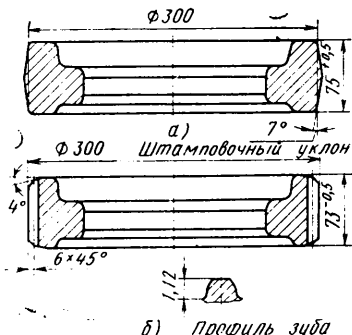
Изменение процесса изготовления ведомой цилиндрической шестерни:
